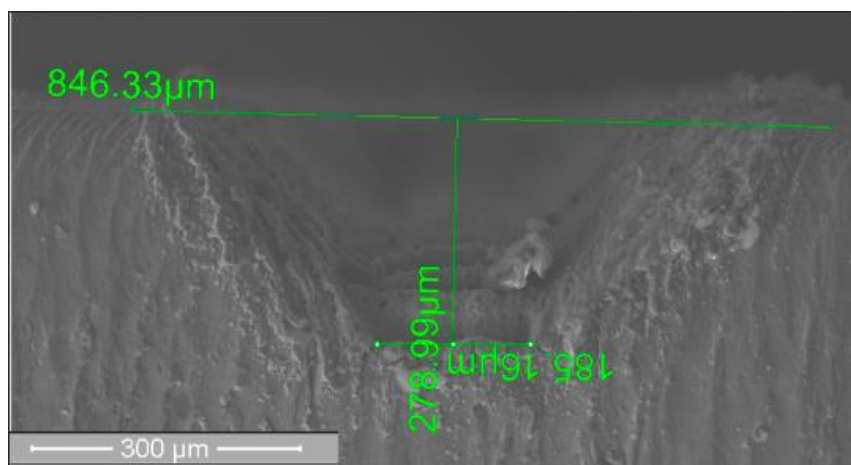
Торец образца из стали 12X18Н10Т с параметрами для получения резьбового соединения M3
